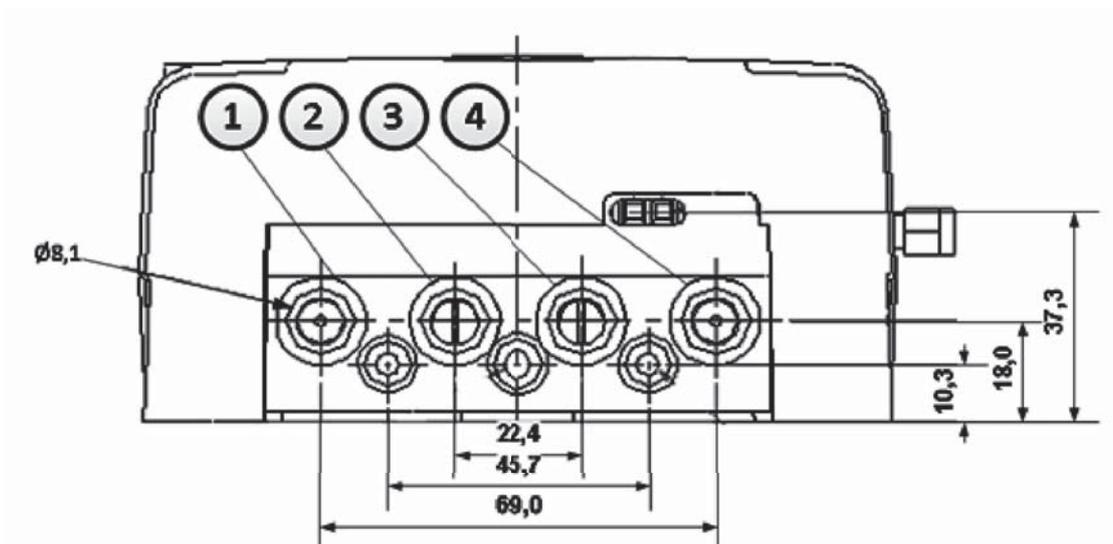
Габаритные и установочные размеры клеммного блока счетчика AS220B
